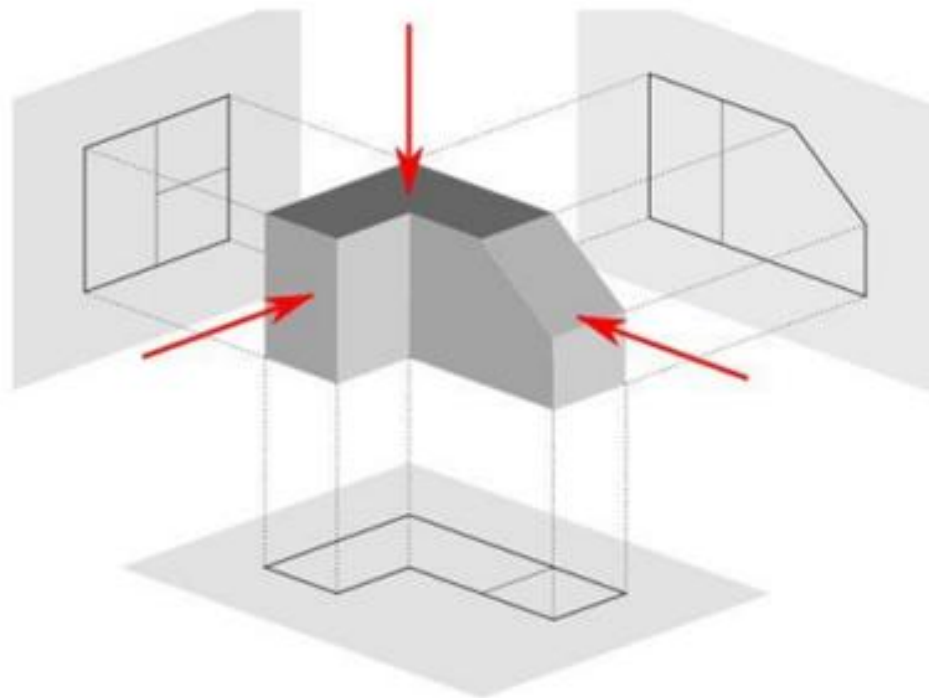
projection orthogonale d'un objet sur 3 plans de projection
